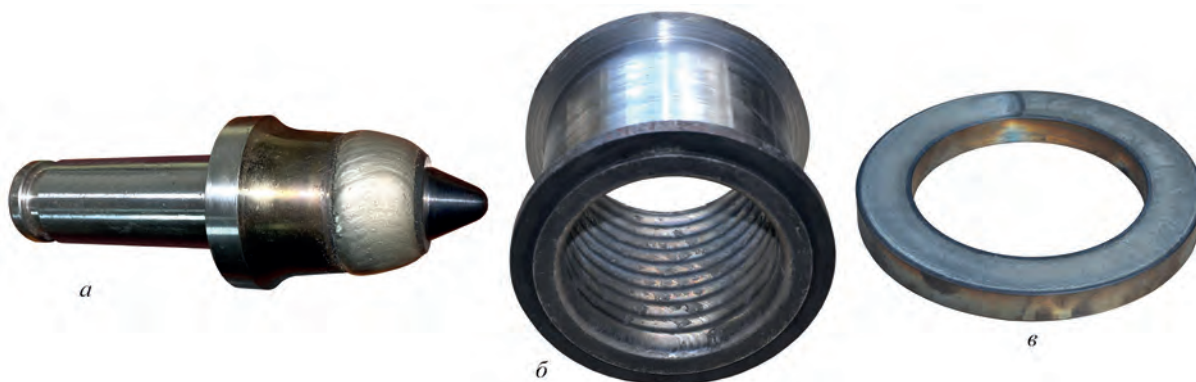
Примеры деталей, наплавленных композиционным сплавом: *а* – резец угольного комбайна; *б* – корпус размольного оборудования; *в* – стабилизирующее кольцо насоса
